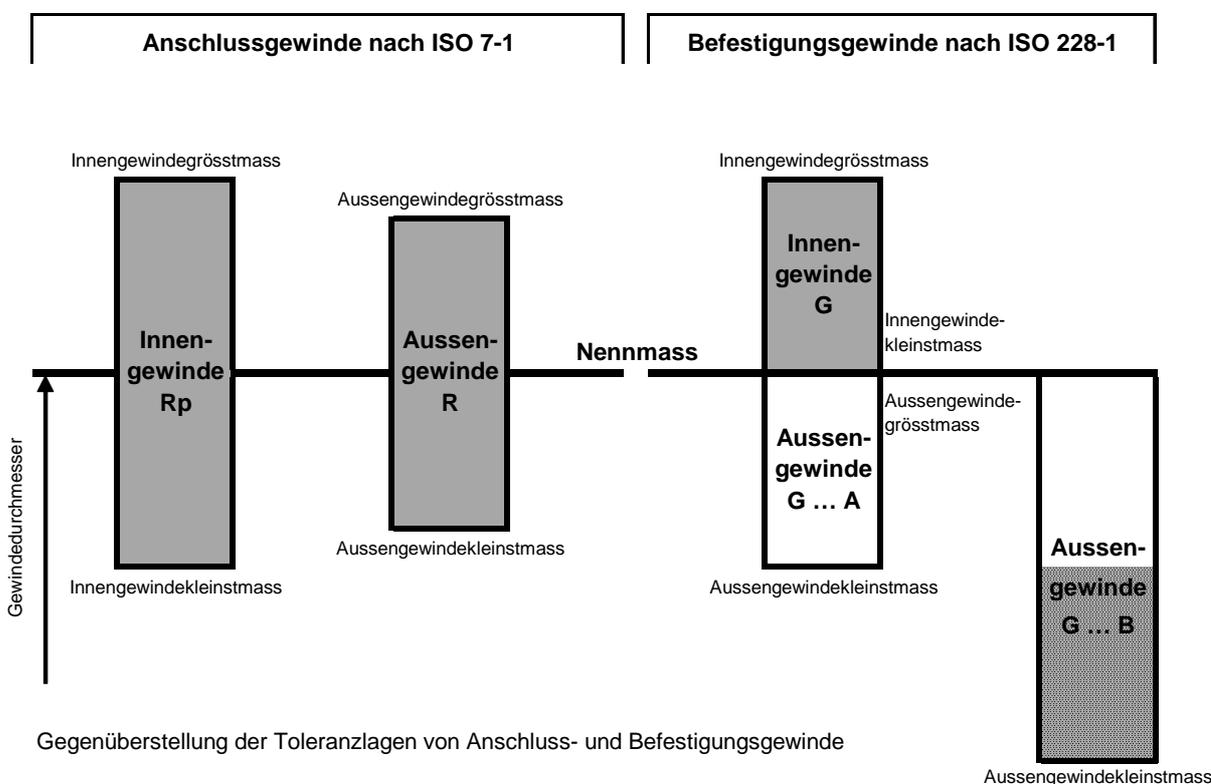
Gegenüberstellung der Toleranzlagen von Anschluss- und Befestigungsgewinde
